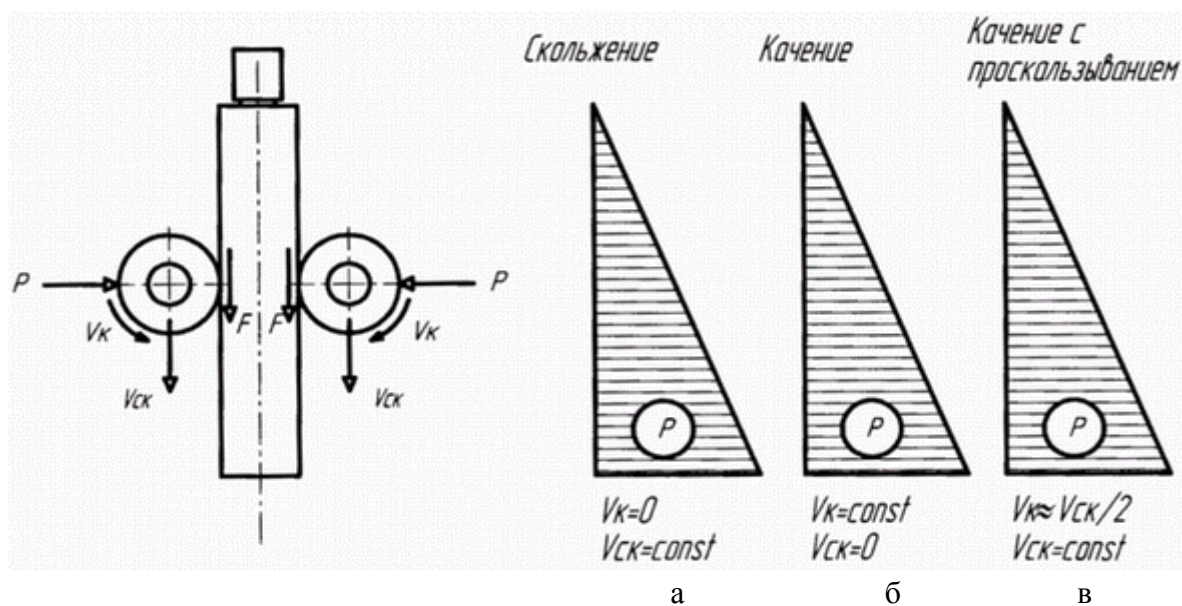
Схема испытаний на трение перекрещивающихся цилиндров:
